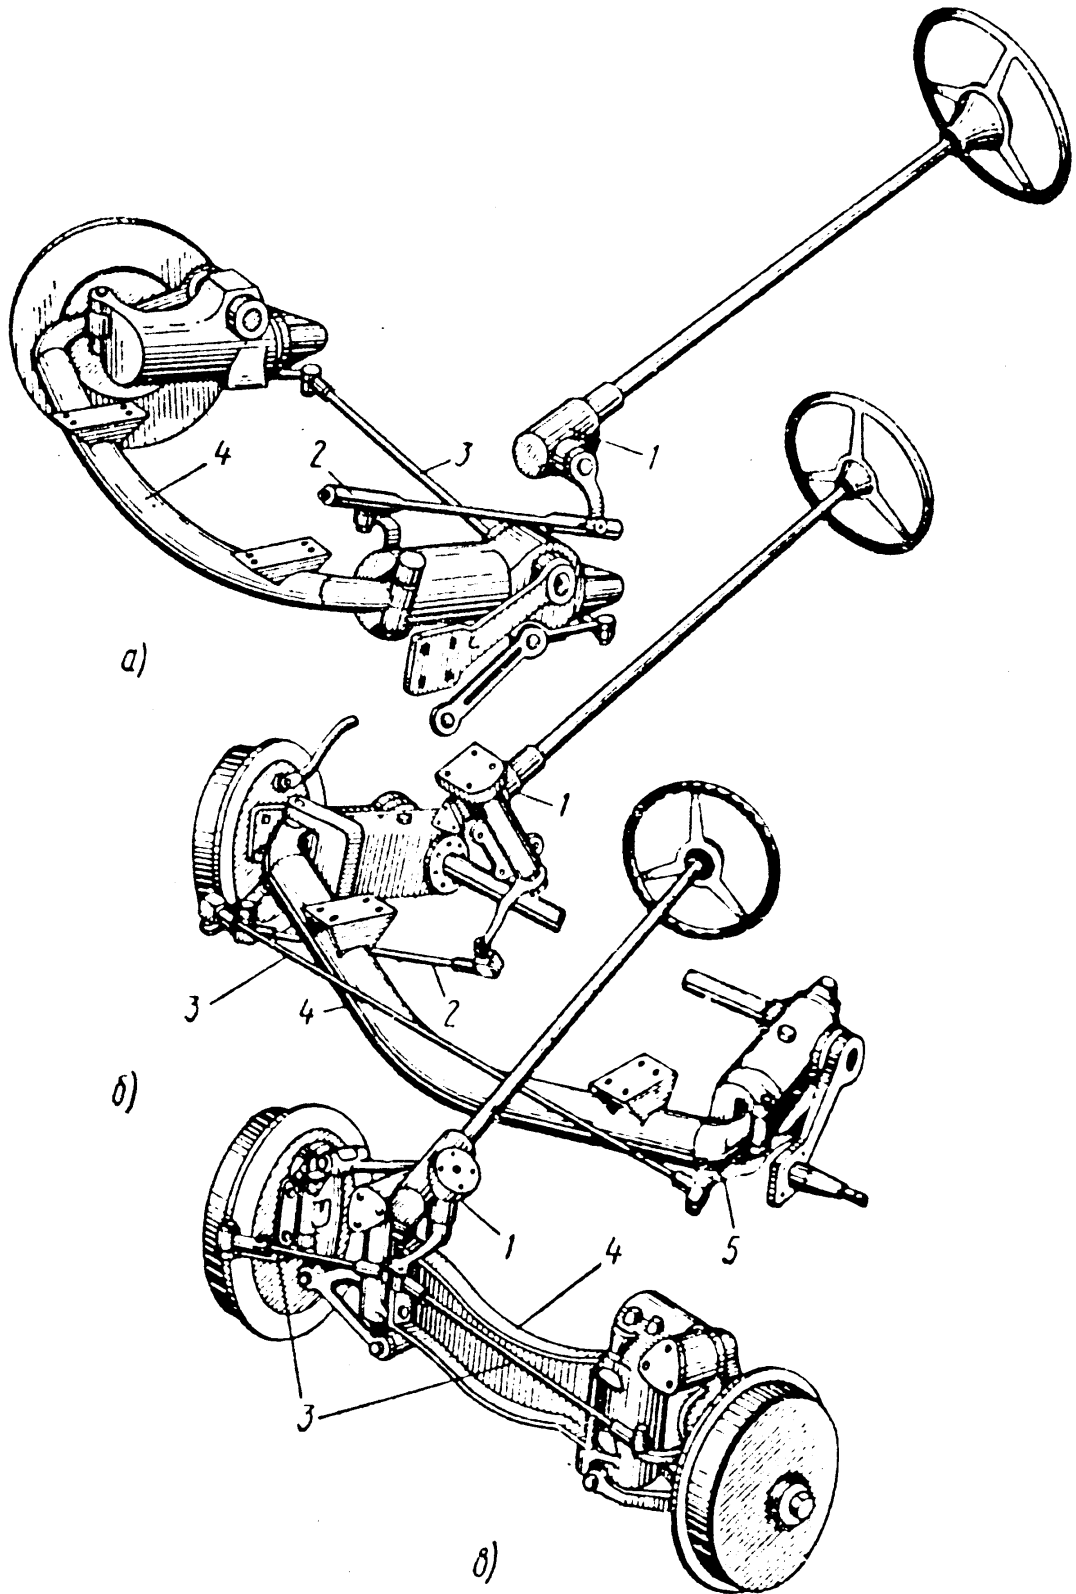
Схема компоновки елементів рульового приводу.
